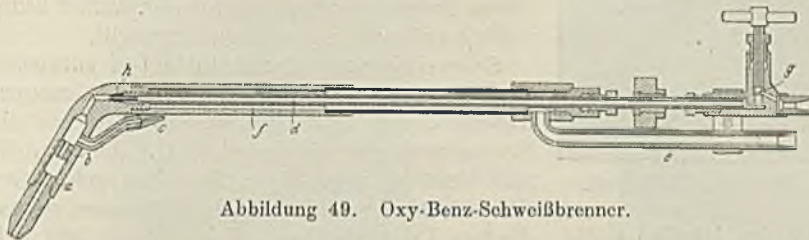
Oxy-Benz-Schweißbrenner.
